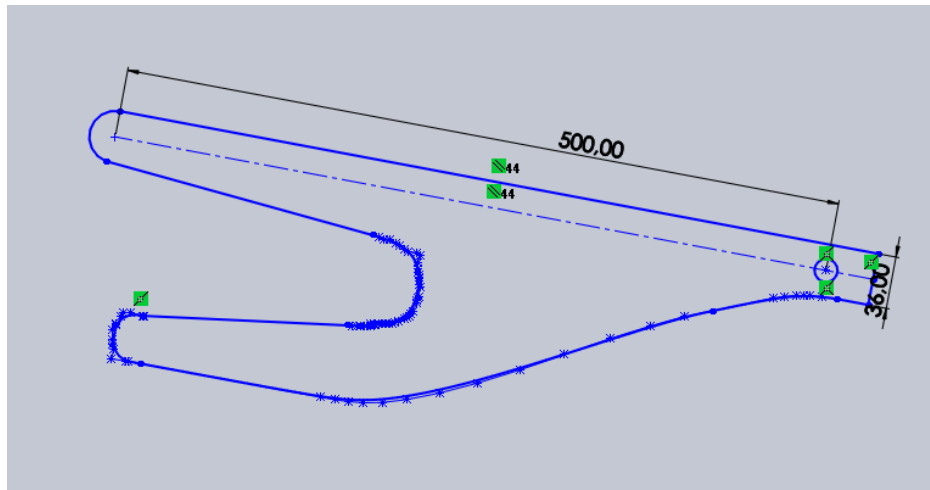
Diseño inicial en SolidWorks de la vista lateral izquierda del basculante. [2]
